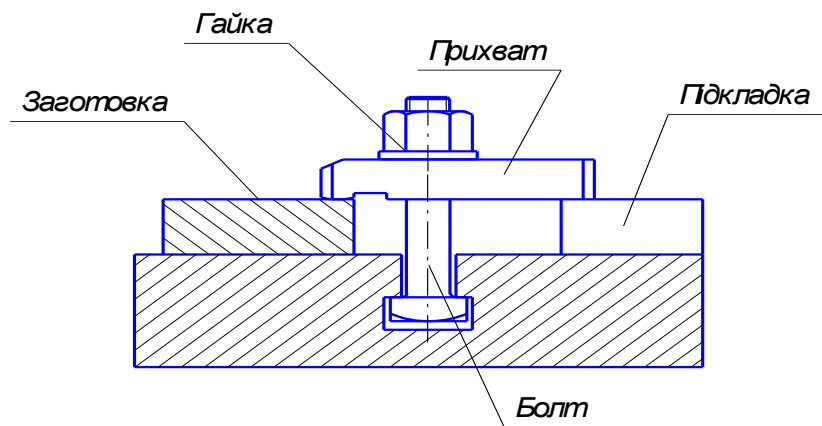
Закріплення заготовки на столі фрезерного верстата
